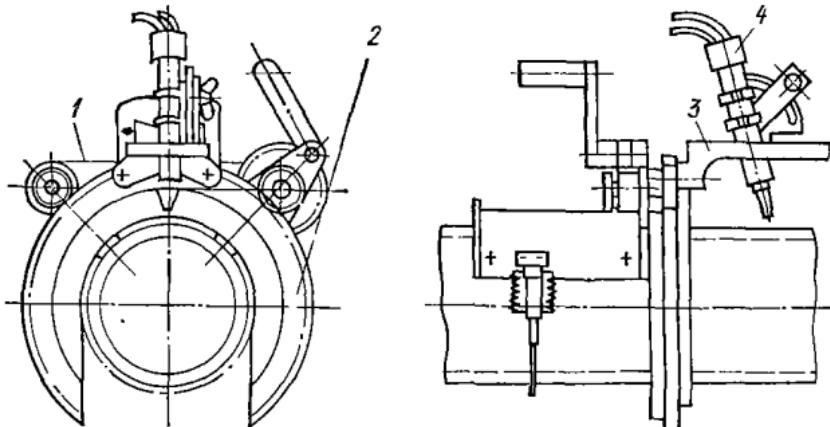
Устройство МУРТ-219 для газопламенной резки труб в монтажных условиях:
